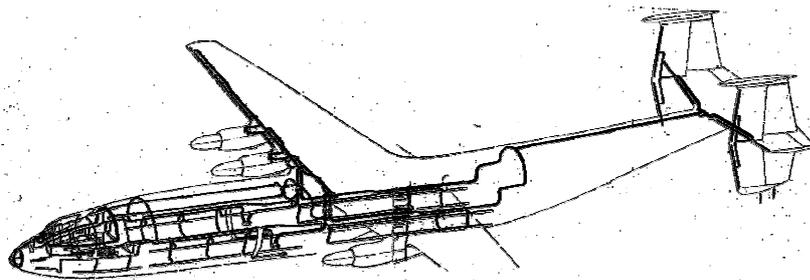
Схема сварного воздушного трубопровода из сплава OT4-0 противообледенительной системы широкофюзеляжного транспортного самолета
